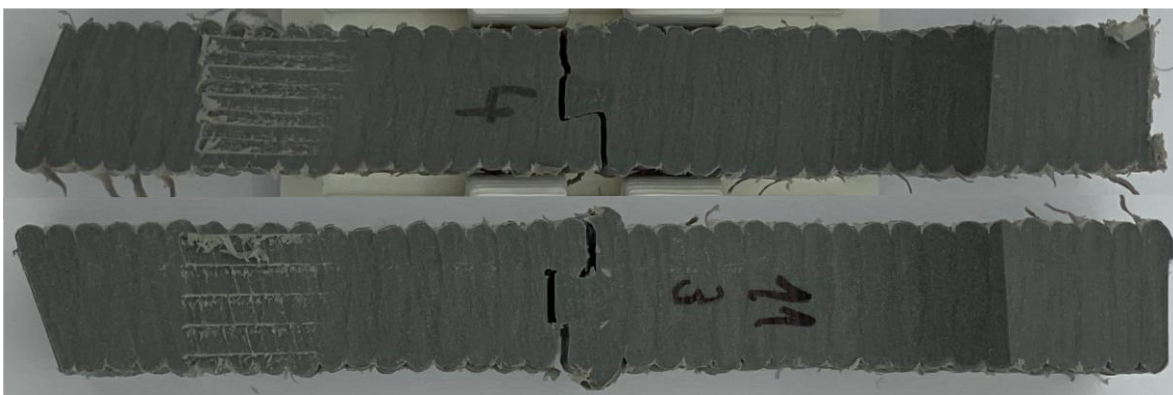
Mechanismus porušení spoje typu vysunutí
